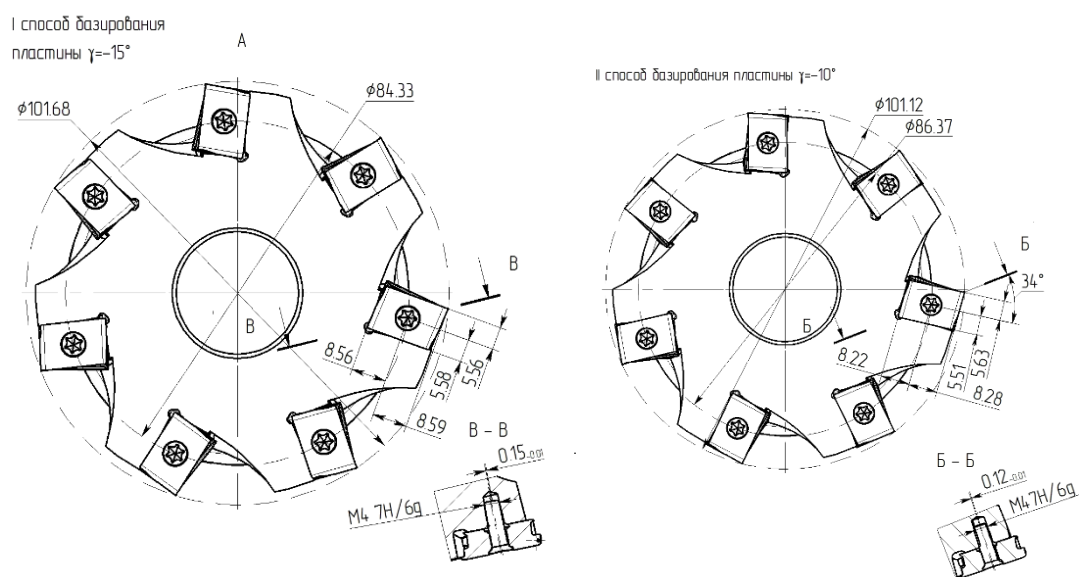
Способы базирования тангенциальной пластины в сборной фрезе
